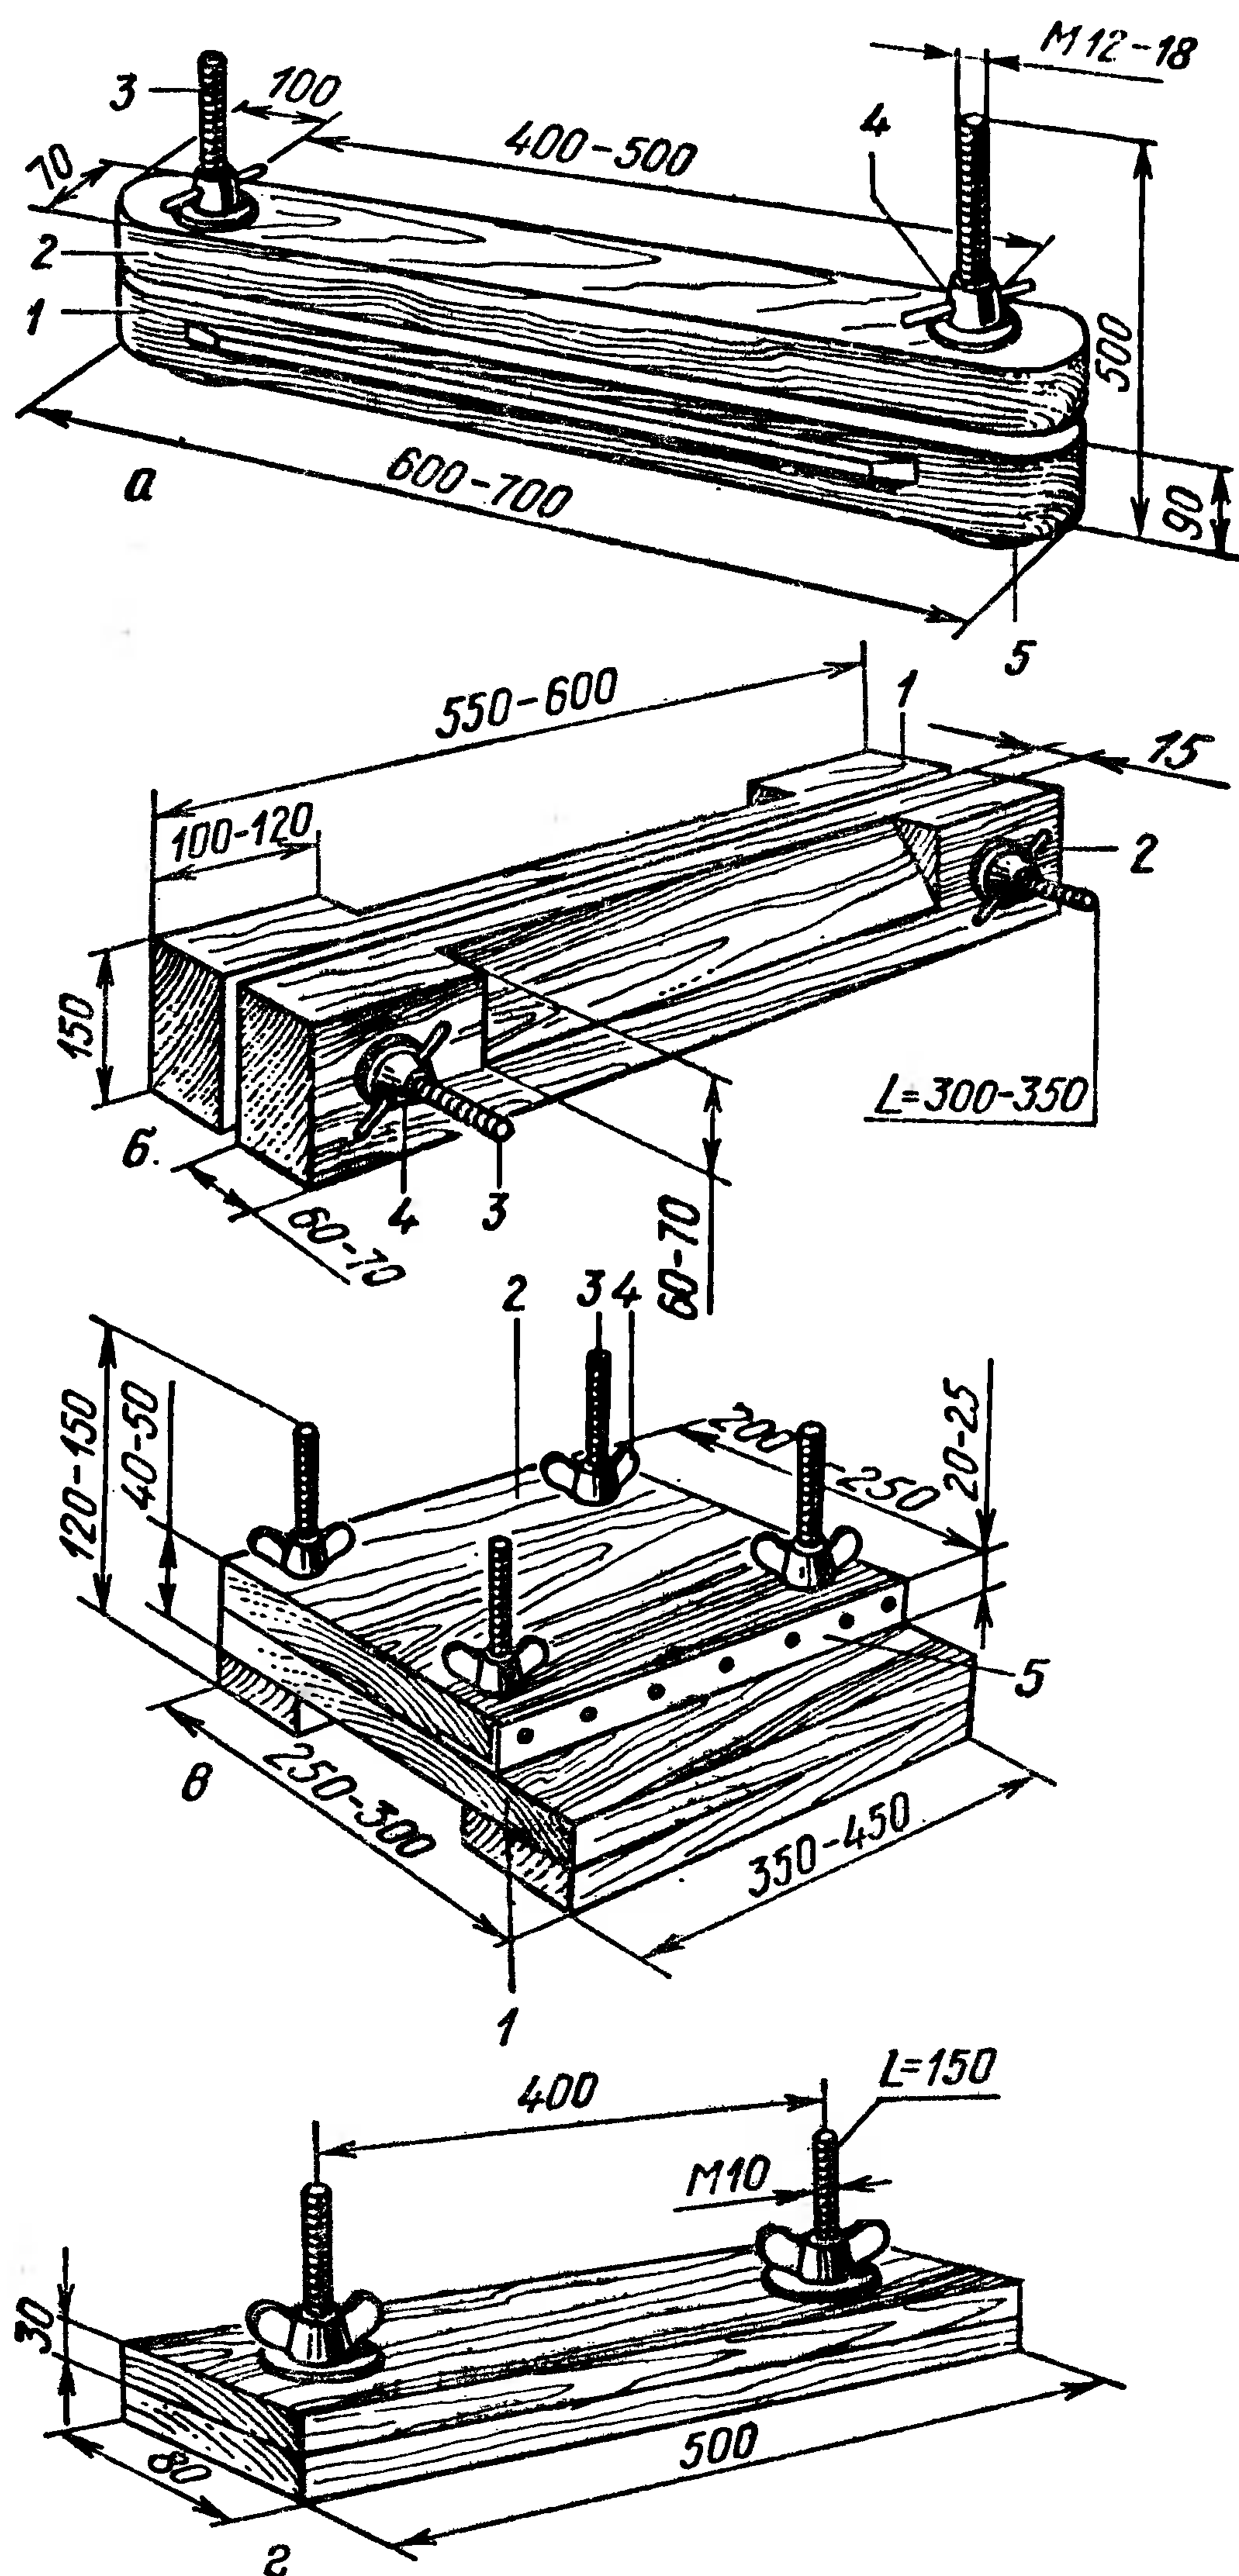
Переплетные тиски: а — универсальные тиски; б — переплетный пресс; 1 — неподвижный брусок; 2 — перемещающийся брусок; 3 — болт; 4 — зажимная гайка; 5 — направляющий полз для гобеля; в — обжимной пресс, приспособленный для обрезки книг переплетным или круглым ножом; 1 — основание; 2 — прижимная доска; 3 — болт; 4 — гайка; 5 — металлический уголок; г — обжимной пресс для вспомогательных работ.
